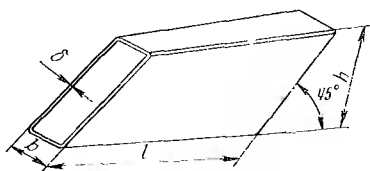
Усилительная вставка при сварке встык труб каркаса автобусов ЛАЗ и ЛАЗ
